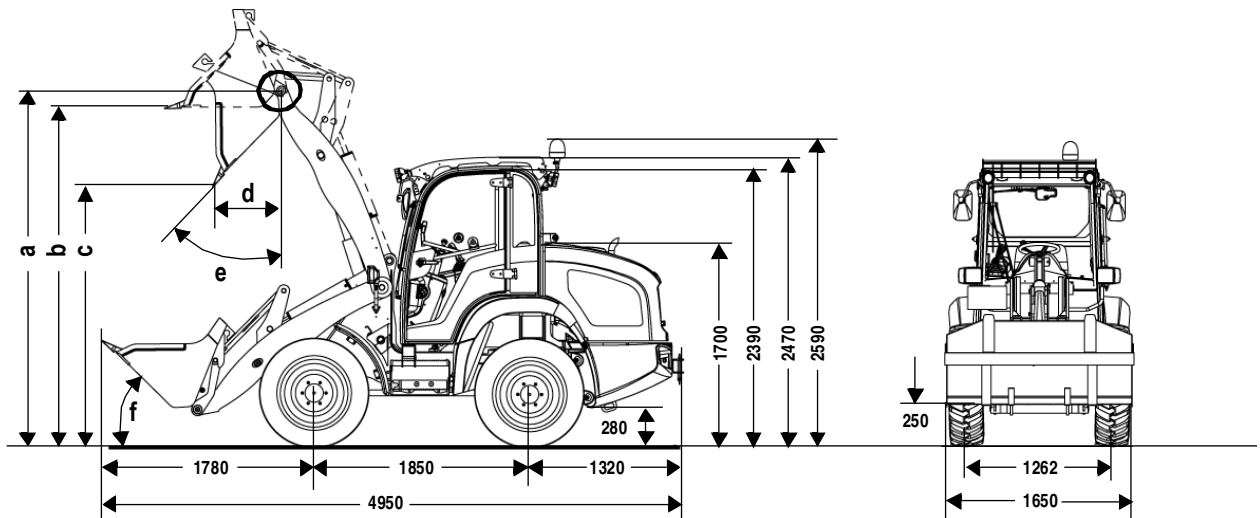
Fahrzeug-Abmessungen mit Schaufel
